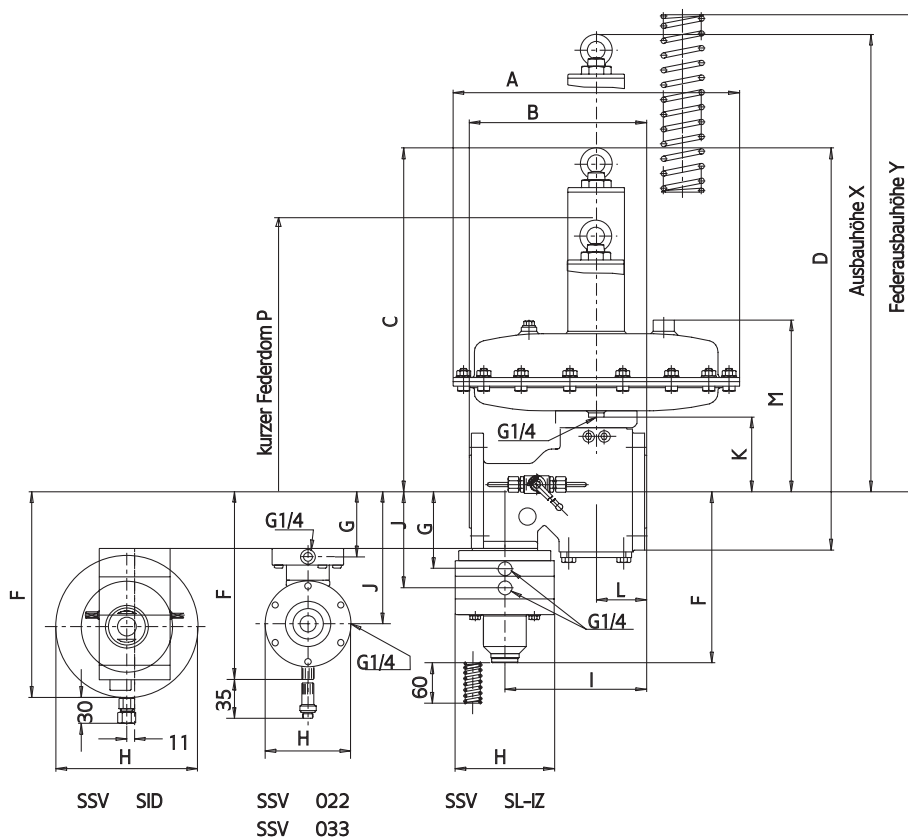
Gasdruckregelgerät RR16 mit SAV - Abmessungen
